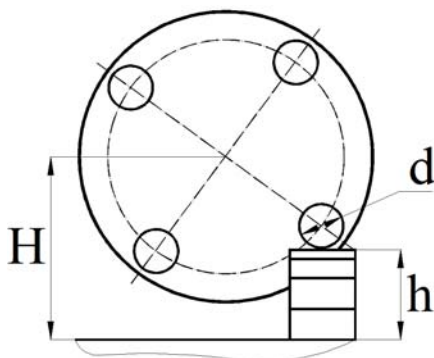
Схема настройки делительного синусного приспособления
